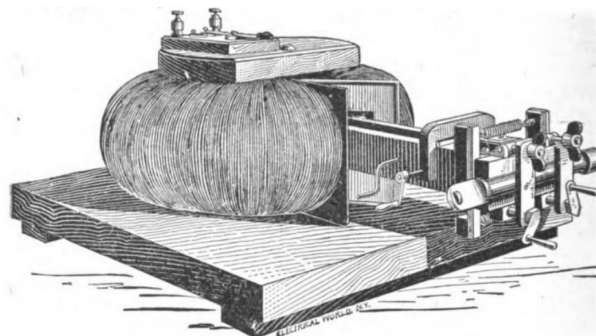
Primeiro transformador do processo de soldagem por resistência (ENG-TIPS, 2019).
